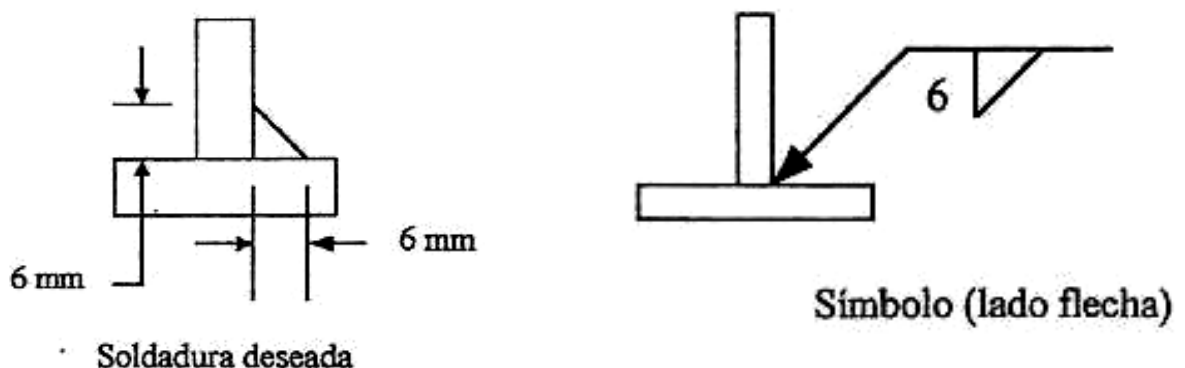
SOLDADURAS DE FILETE DEL LADO DE LA FLECHA.
